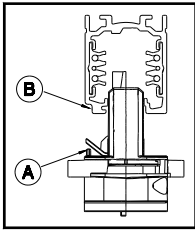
Chiave meccanica - Pic. 3 Mechanical key
